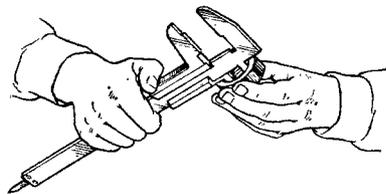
Прием измерения диаметра резьбы штангенциркулем
